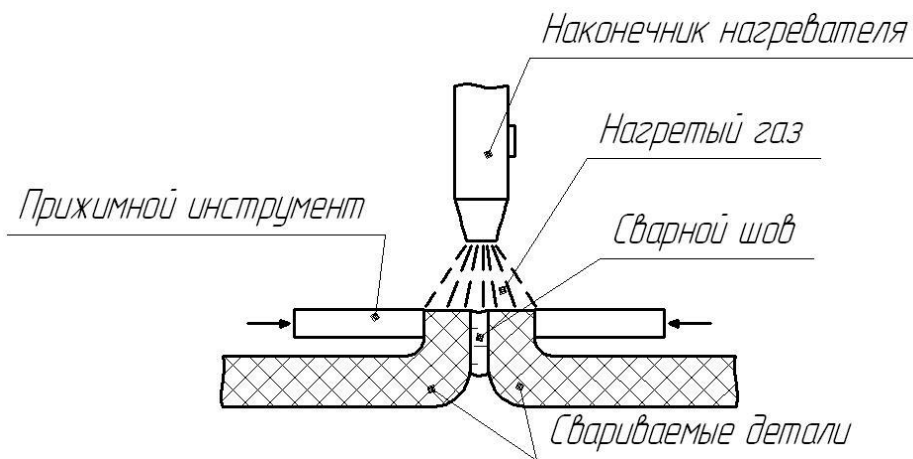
Сварка нагретым газом без применения присадочного материала
